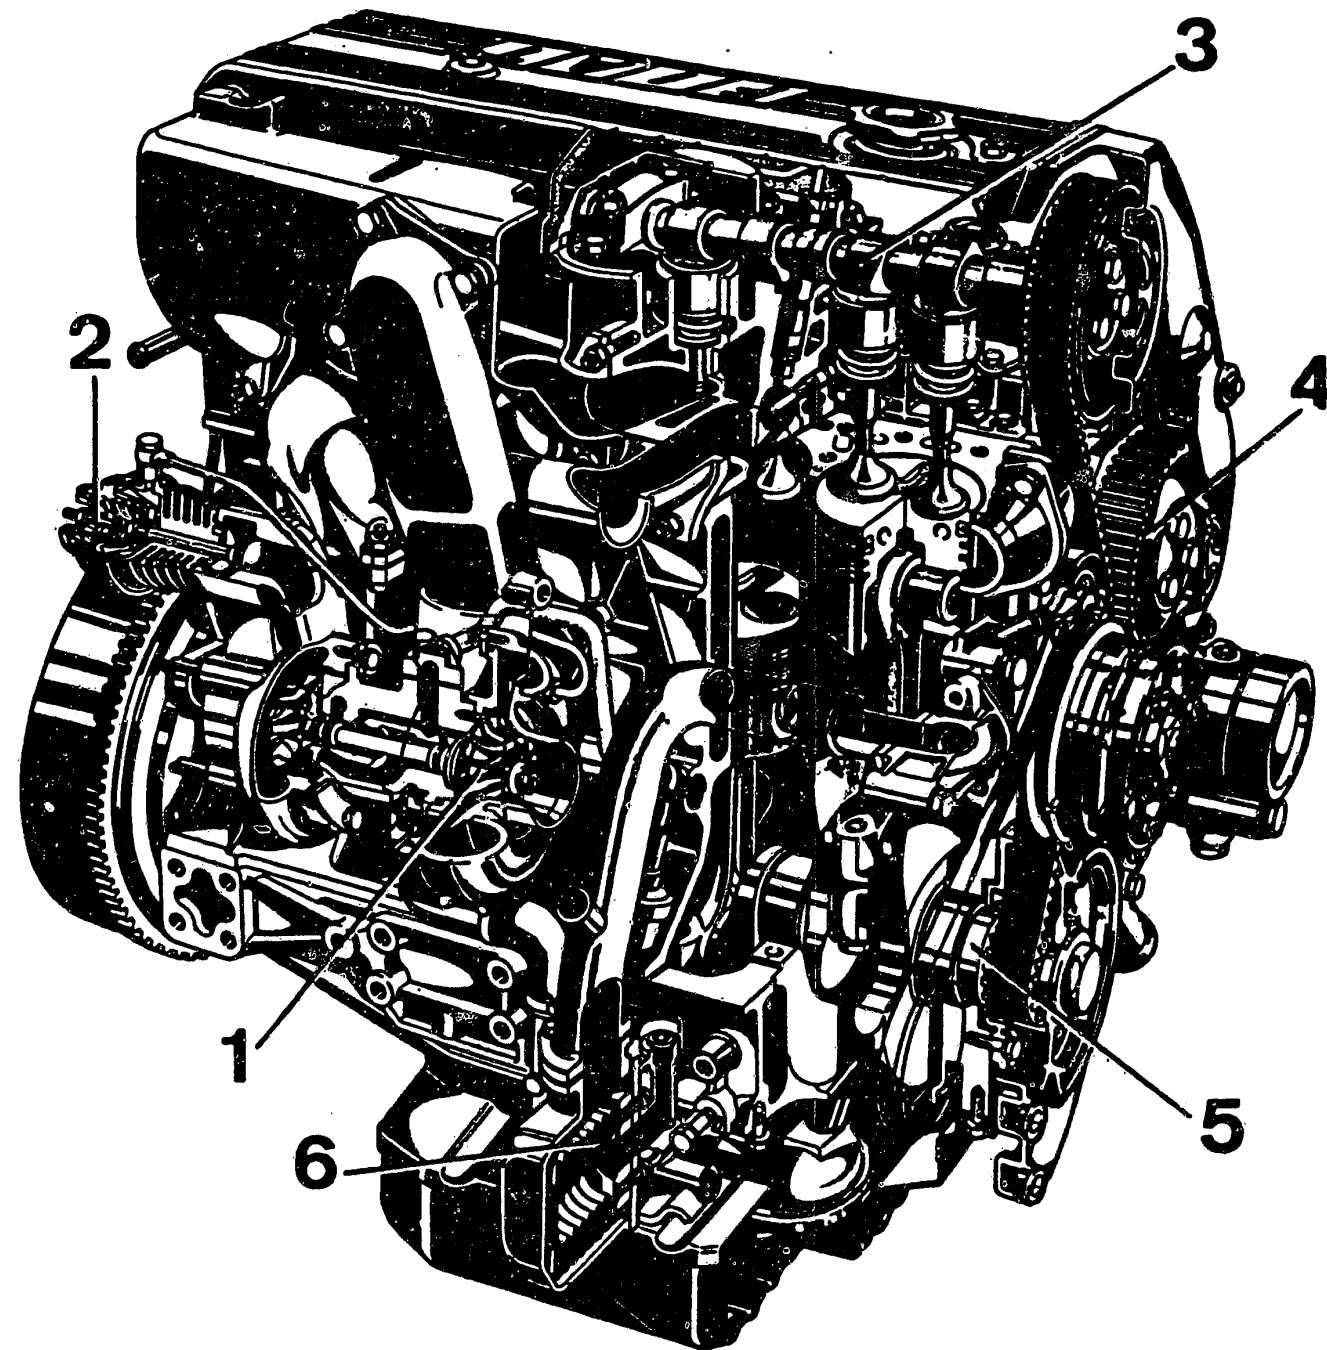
Turbo-Dieselmotor 2500, teilweise aufgeschnitten: 1 Turbolader – 2 Waste Gate-Ventil – 3 obenliegende Nockenwelle – 4 Einspritzpumpen-Antriebsrad – 5 Kurbelwelle – 6 Wärmetauscher Öl-Wasser.
